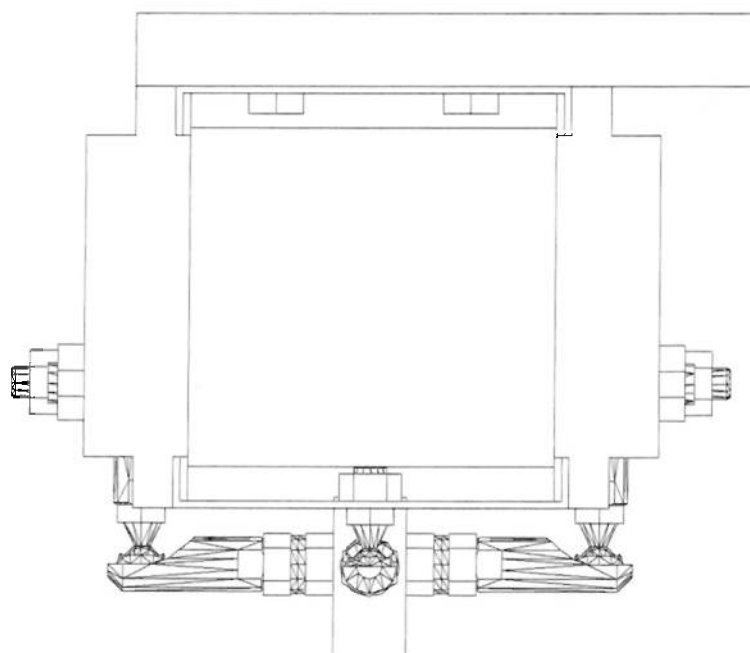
Desenho de conjunto do quadril - vista isométrica
